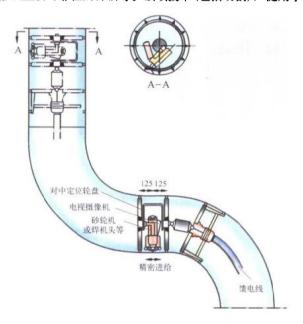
核辐射环境条件下管道内焊接修理用灵巧焊接设备
